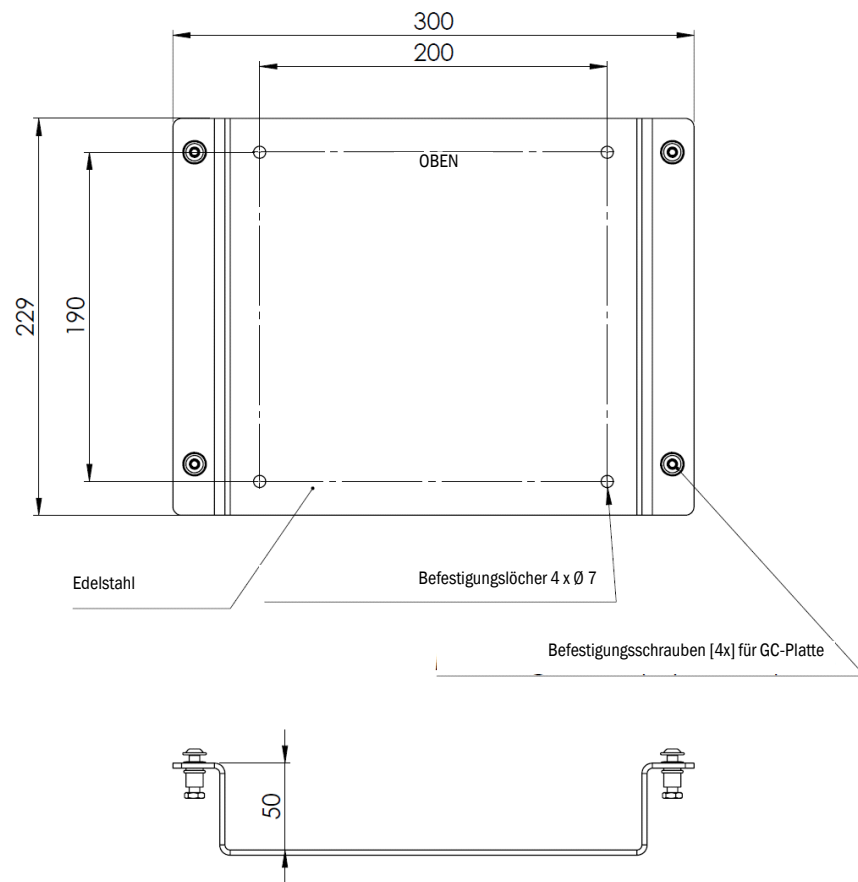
Optionale Wandmontageplatte (Abmessungen und Montage)
